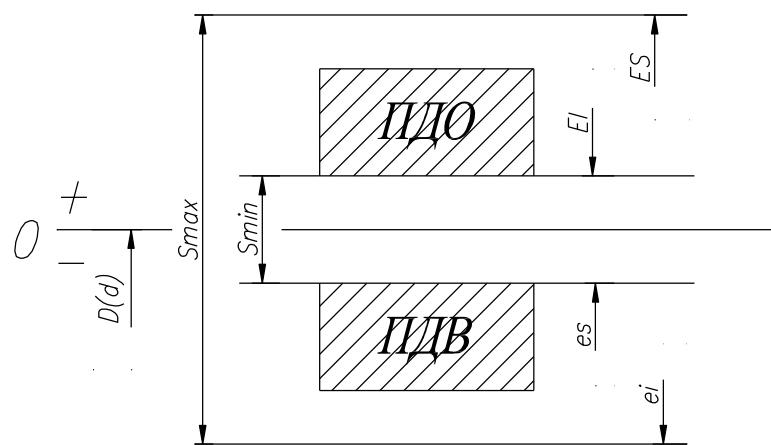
Схема розташування полів допусків з'єднання з зазором
